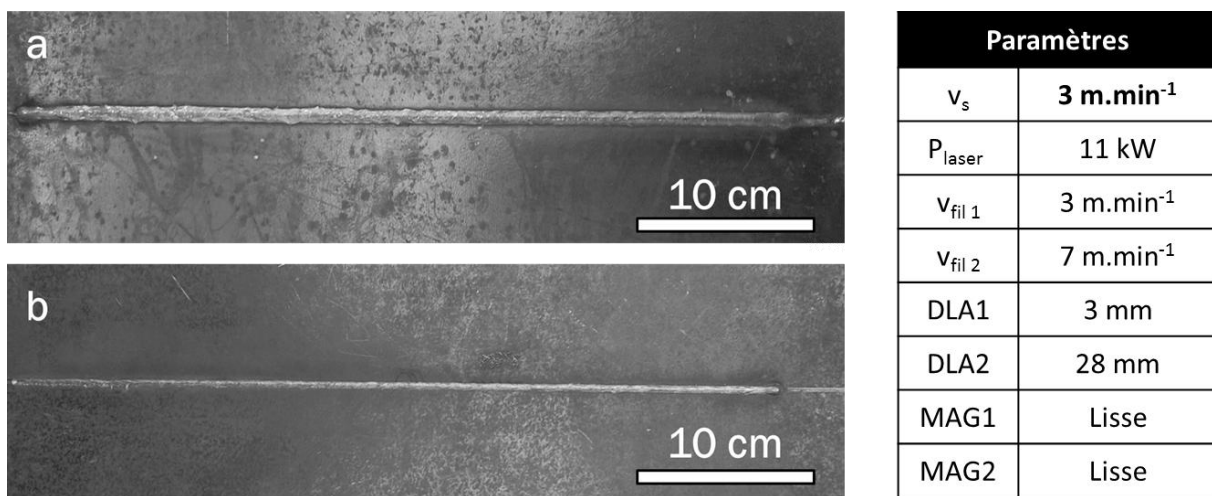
Vues endroit (a) et envers (b) du cordon hybride bicathodes MAG-laser-MAG produit à forte vitesse de soudage
